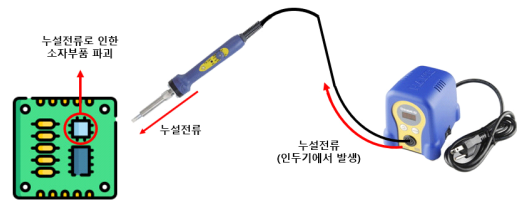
인두기 누설전류로 인한 PCB 소자 부품 파괴
